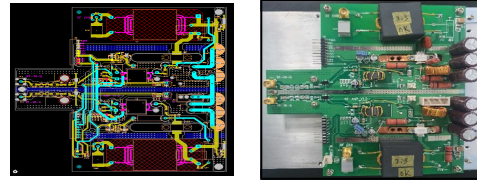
회로 설계를 통한 PCB Artwork 및 PCB 제작
